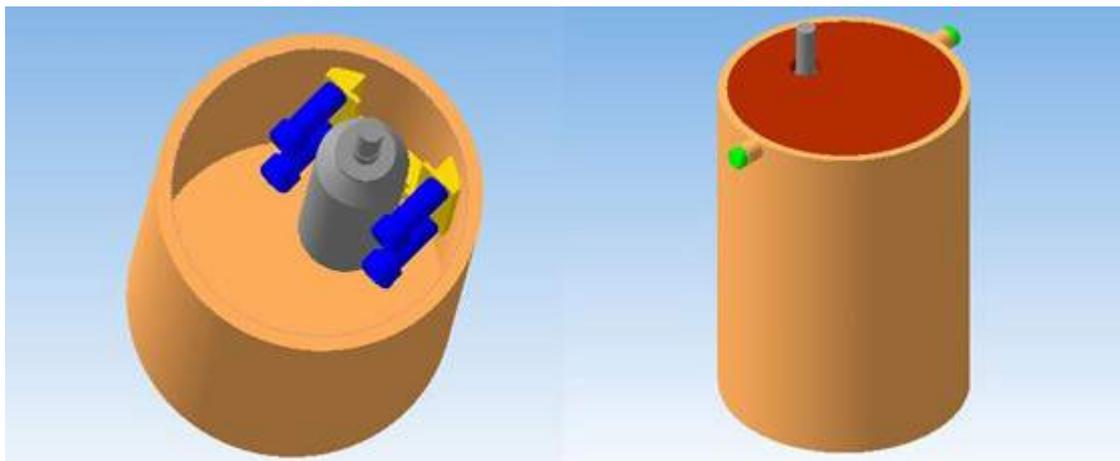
Модель винтового забойного двигателя: установленный ротор с упором для эластомера, прижимаемый четырьмя винтами (слева) и корпус модели в закрытом варианте (справа)
